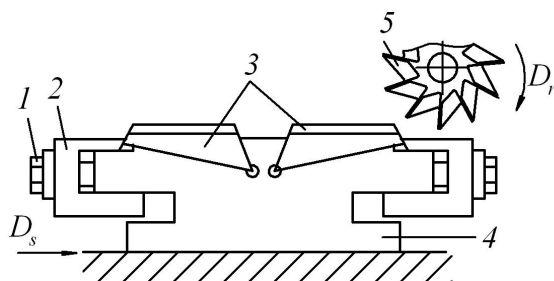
Схема фрезерования рифлений на ножах в многоместном приспособлении: 1 – болт; 2 – прижим; 3 – заготовки; 4 – корпус; 5 – фреза
